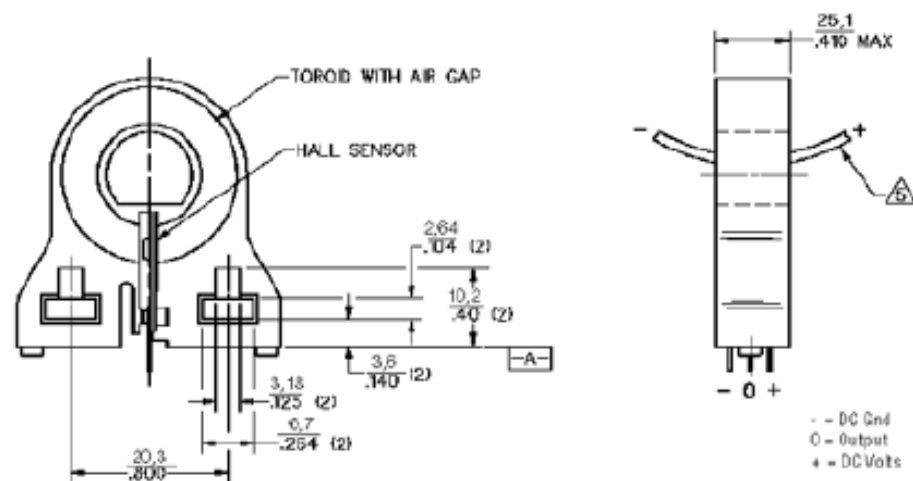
Dimensiones del sensor de corriente lineal CSLA2CF [55]
